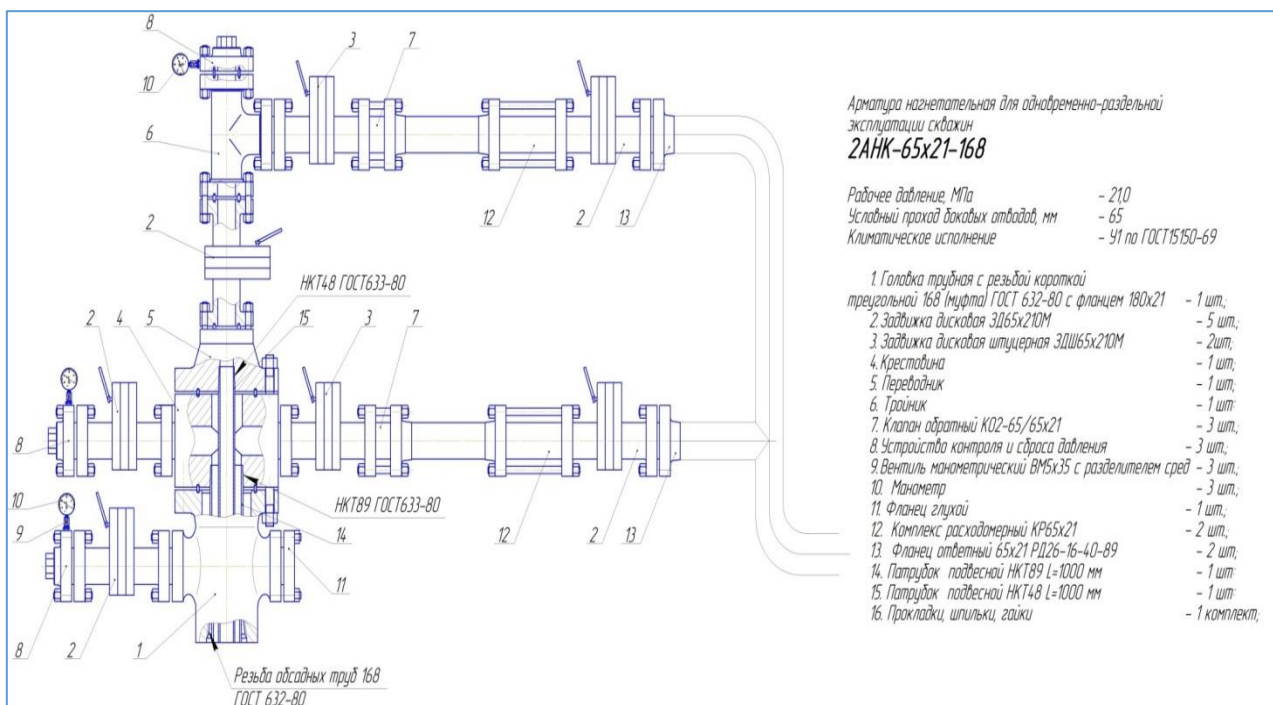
Конструкция арматуры устьевого оборудования нагнетательной скважины 2АНК-65x21-168
